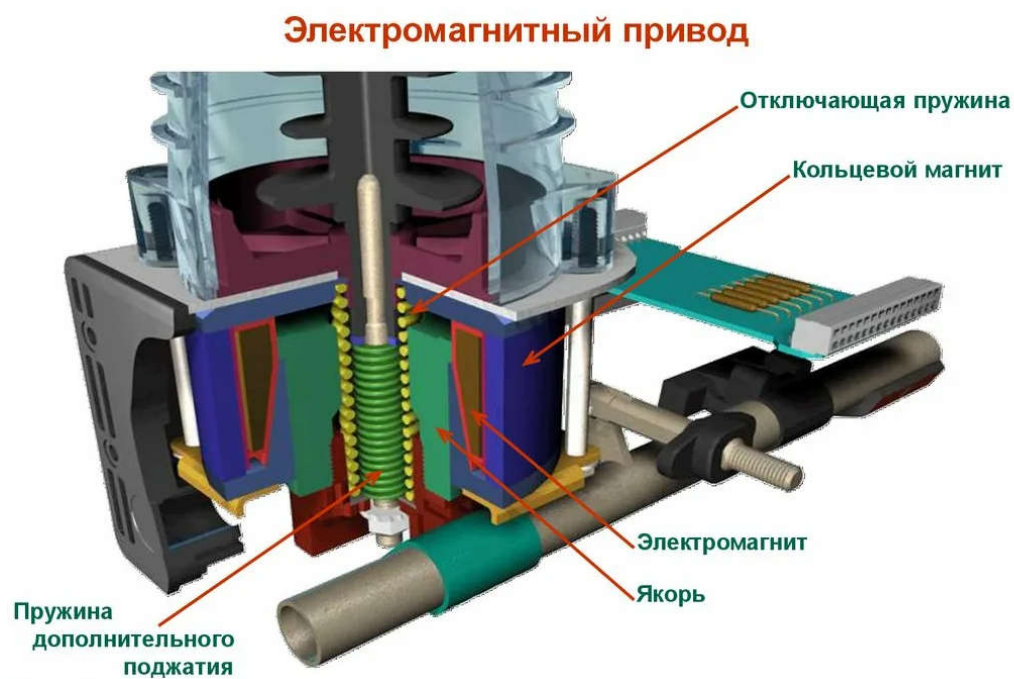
Электромагнитный привод выключателя BB-TEL
